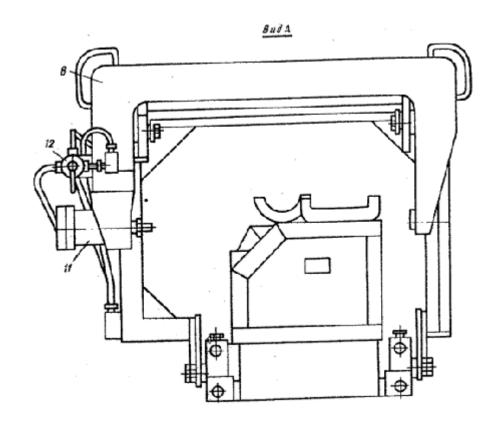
Вид А стенда для разборки и сборки коробок передач
